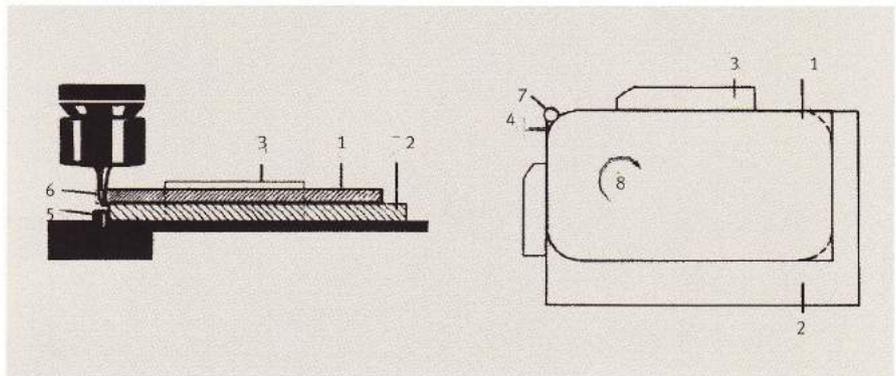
Принцип верхнего фрезерования по шаблону: 1 – заготовка, 2 – направляющая опора, 3 – ограничитель, 4 – шаблон, 5 – направляющий стержень, 6 – фреза, 7 – рабочая зона фрезы, 8 – подача
